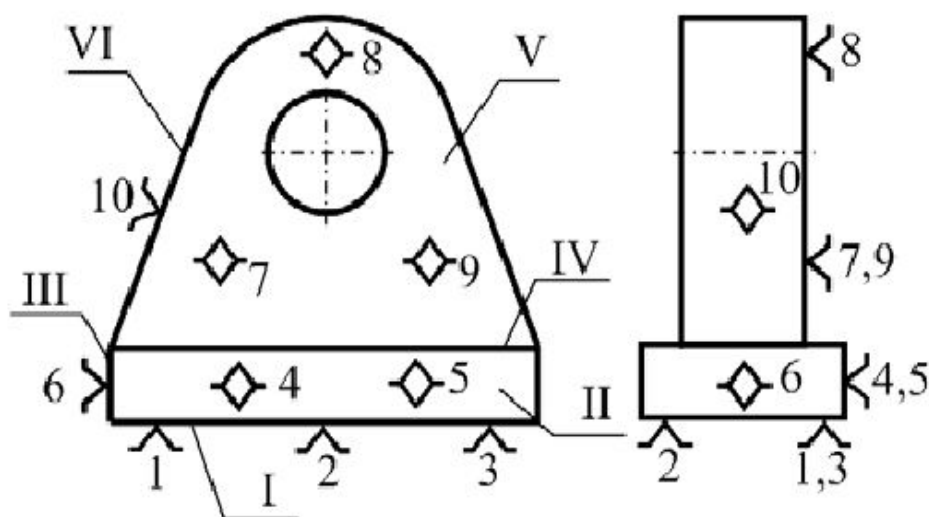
Схема базирования сварной проушины в сборе
